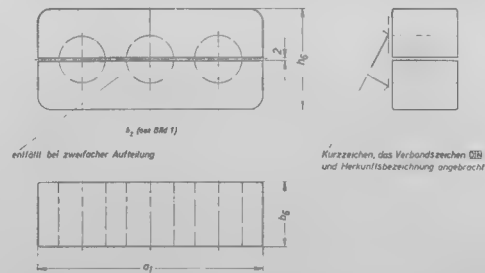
Abzweigmuffen für Fernmeldekabel, Holzfutter für Schutzmuffe.
